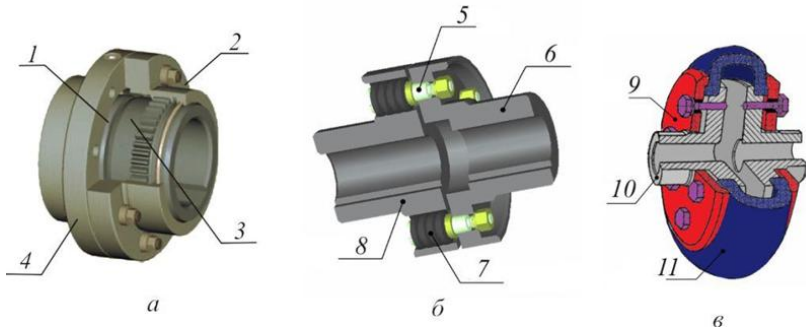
Муфты: а – зубчатая; б – упругая втулочно-пальцевая; в – с резиновым баллоном; 1, 3 – зубчатые втулки; 2, 4 – зубчатые обоймы; 5 – палец; 6, 8 – полумуфты; 7 – резиновое кольцо; 9 – крышка; 10 – полумуфта; 11 – резиновый баллон
